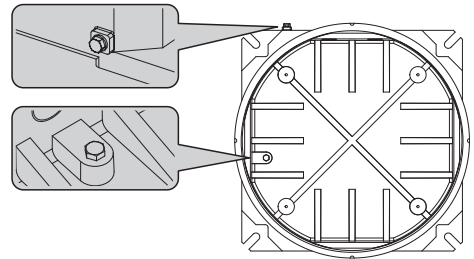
Lagen der externen-internen Schrauben für die Erdung.
